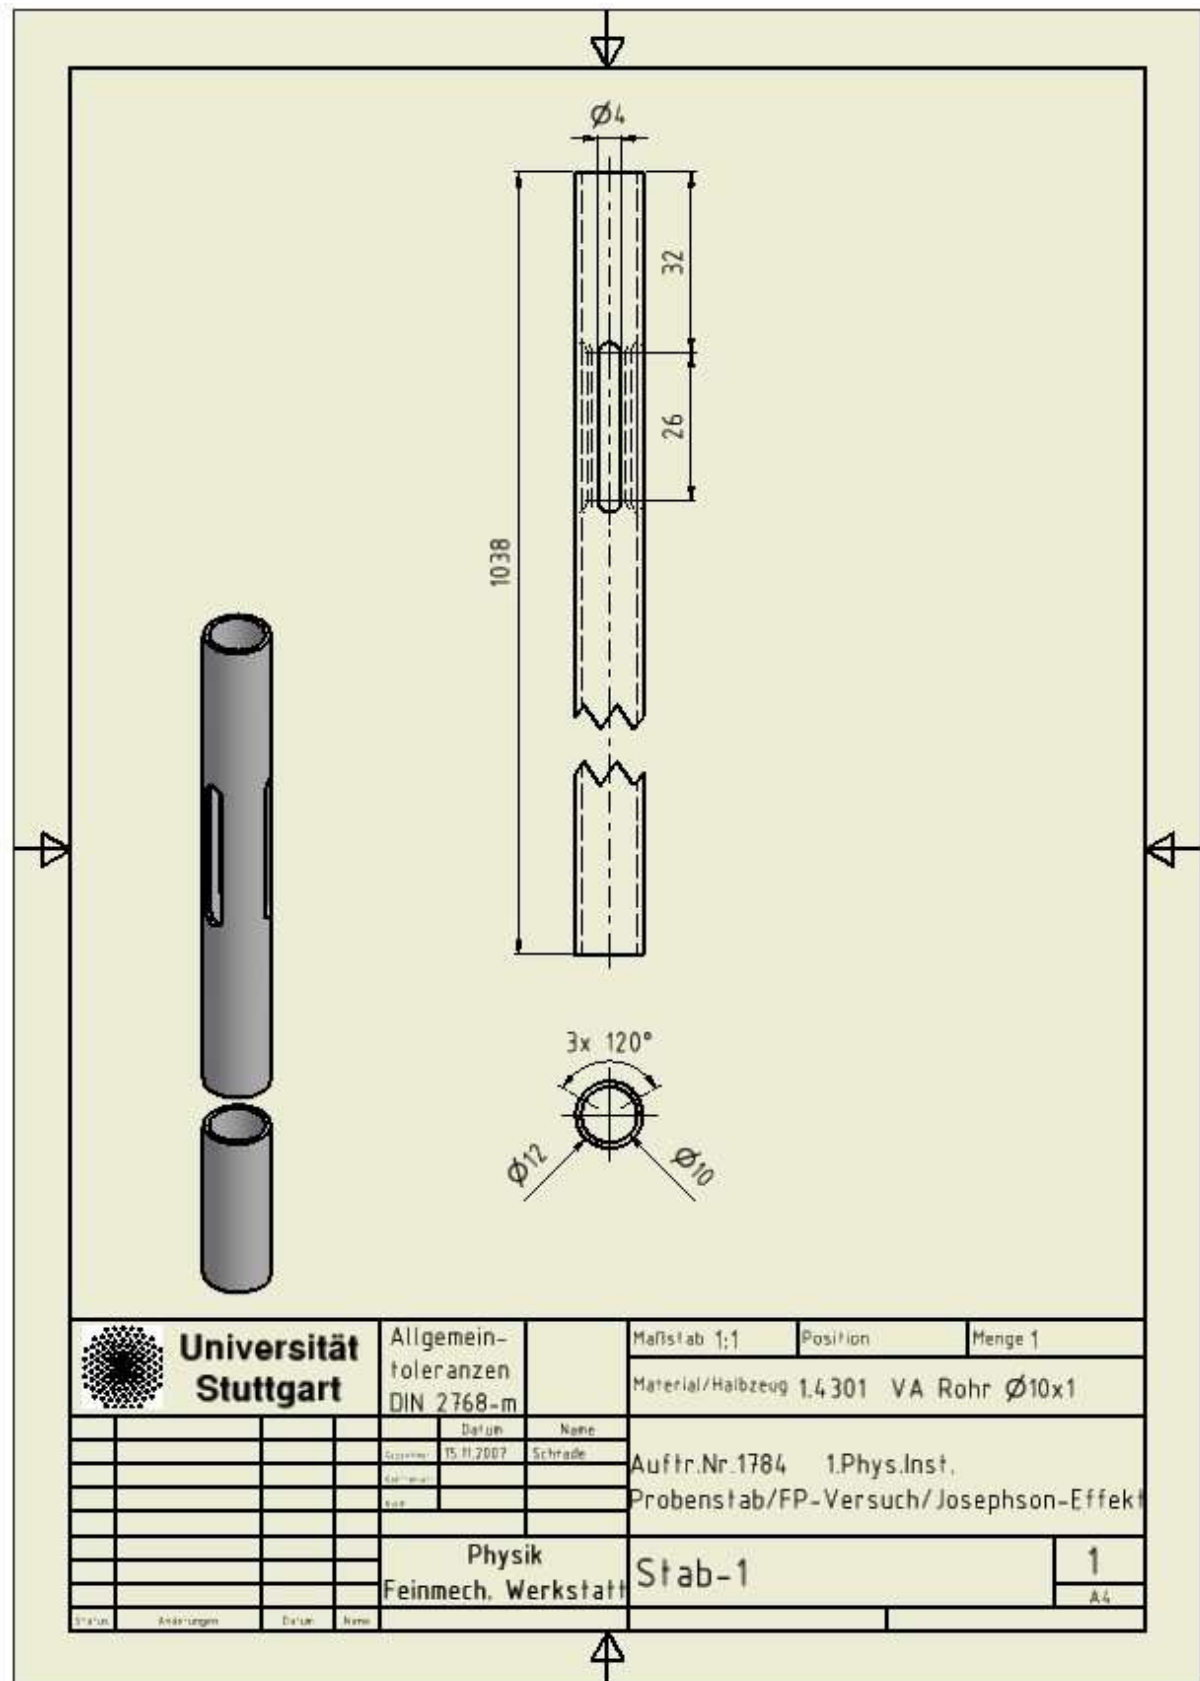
Technische Zeichnung für Edelstahlrohr.
